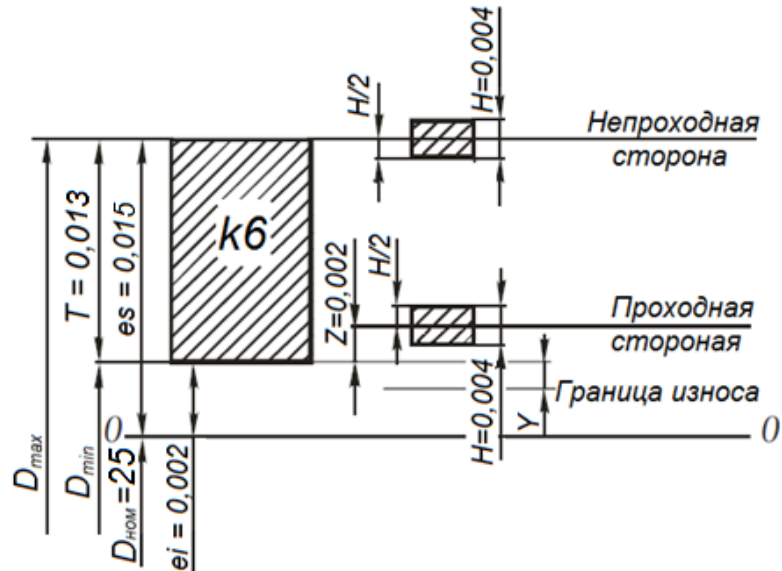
Схема расположения полей допусков вала  $\varnothing 25 k6$  и его рабочих калибров
